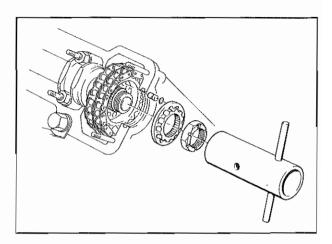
Allentare i dadi di bloccaggio Slacken locking nuts
